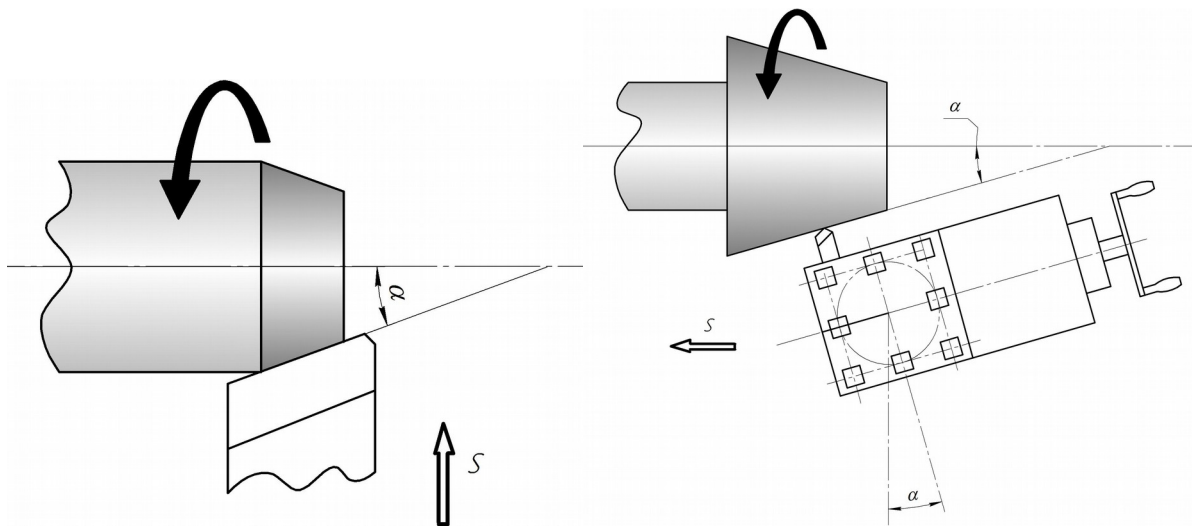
Способи обробки конічних поверхонь: а – широким різцем; б – поворотом верхніх ковзунів супорта
